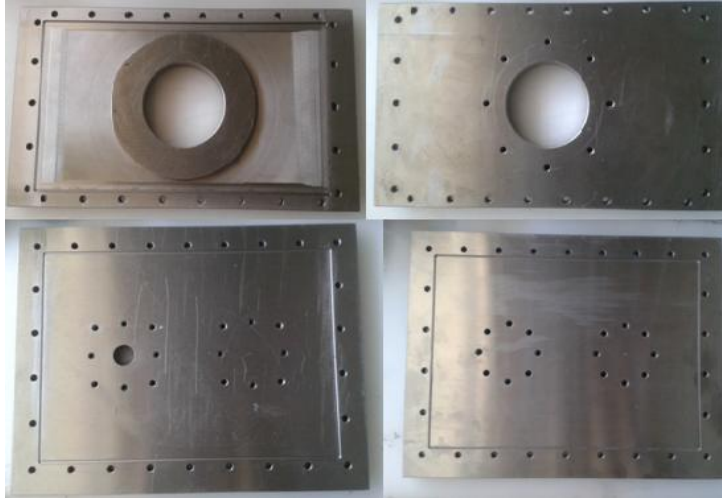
’de motor bloğu ana gövdesi görülmektedir. Motor bloğu ana gövdesi 25x25 mm kalınlığında Ç1040 malzemelerin kaynakla birleştirilmesi ile imal edilmiştir. Motor bloğu ana gövdesi birleşme yüzeyleri çalışma maddesi kaçaklarını en aza indirmek için hassas bir şekilde taşlanmıştır.
